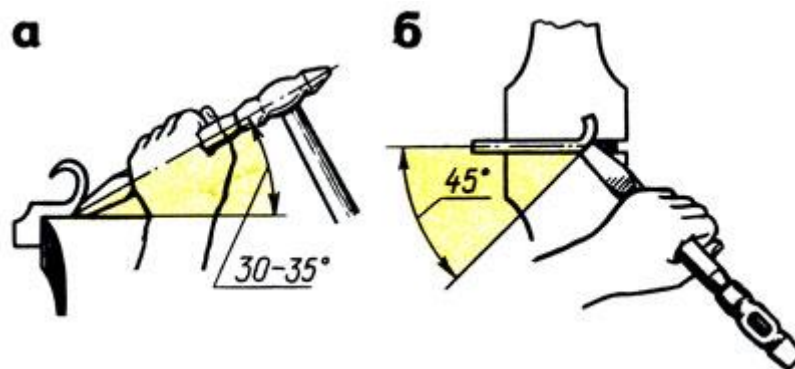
Рубка листового материала: а - угол наклона зубила к обрабатываемой поверхности, б - наклон зубила по отношению к оси губок
